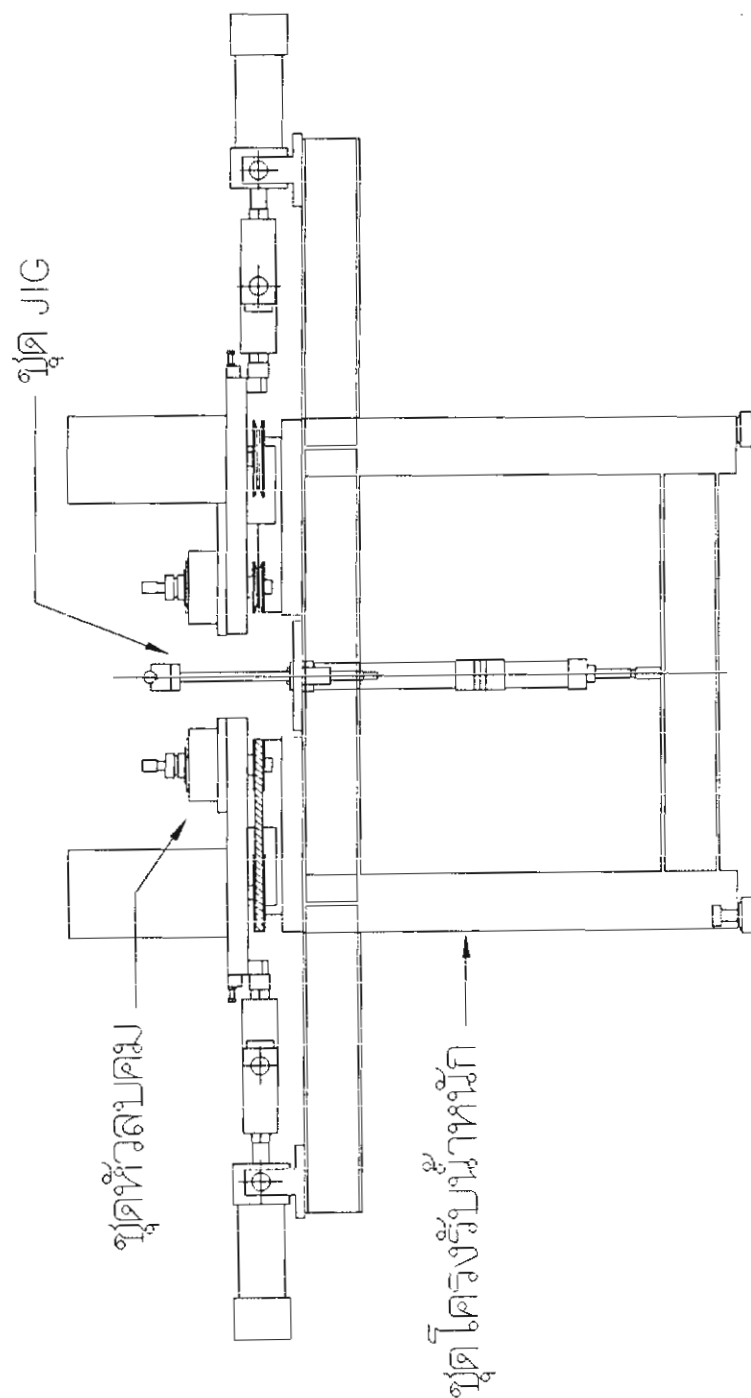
แสดงชุดหัวเจาะ 6 หัวของเครื่อง Drilling Machine
